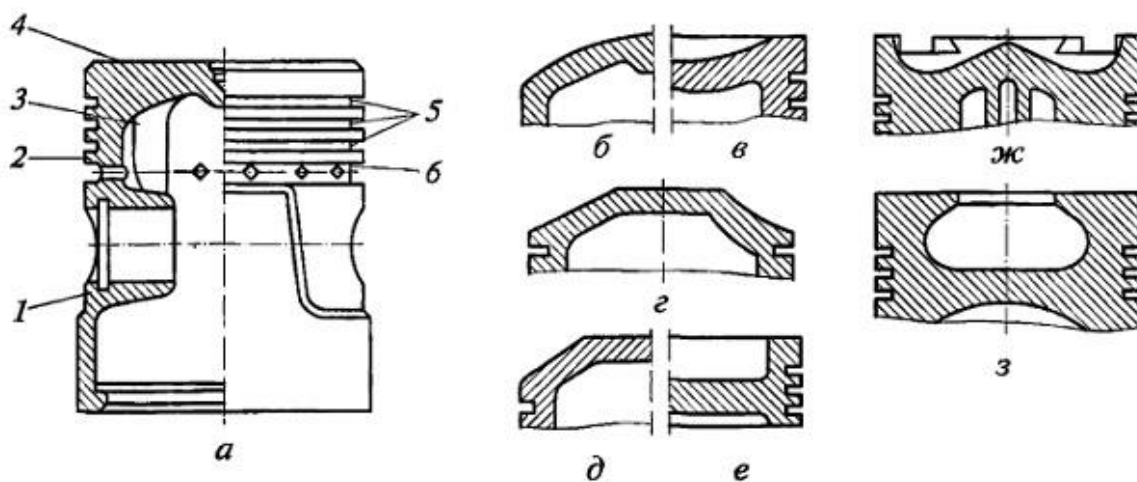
Конструкции поршней с различной формой днища (а—з) и их элементов:
